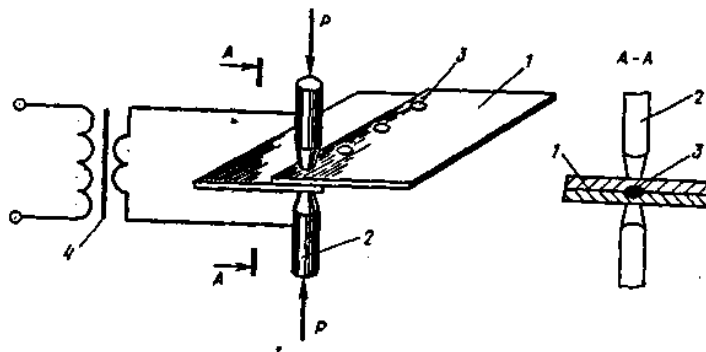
Контактная точечная сварка 1 – свариваемые детали; 2 – электроды точечной сварочной машины; 3 – сварная точка; 4 – трансформатор
